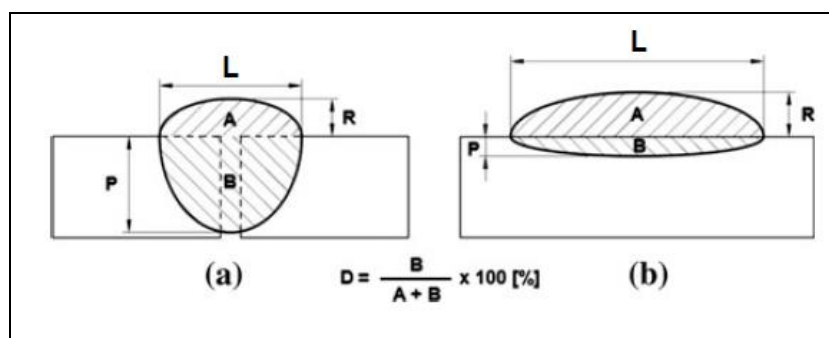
Geometria do cordão: soldagem de penetração (a) e soldagem de revestimento (b).
